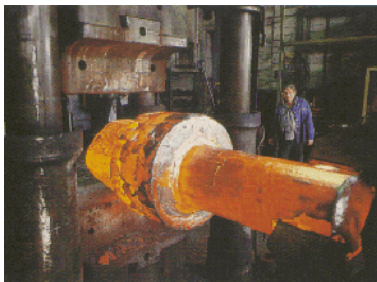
mfZ) Schmiedestück in Bearbeitung (Stooss)
